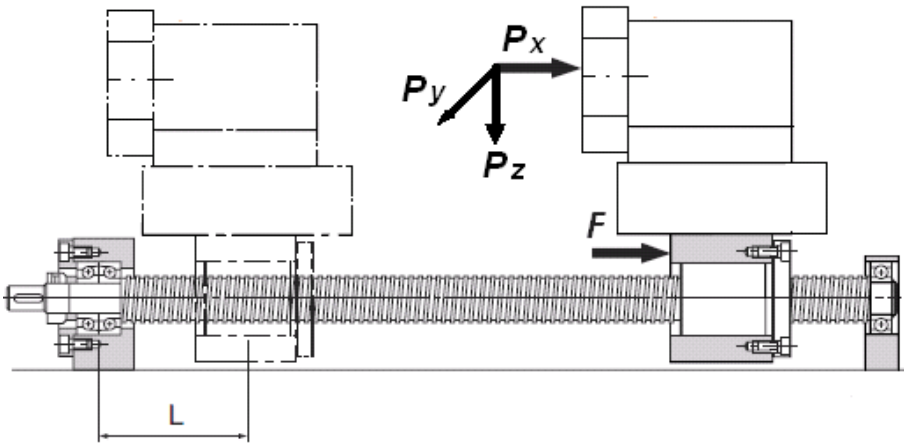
Схема приводу подачі верстата для розрахунку
